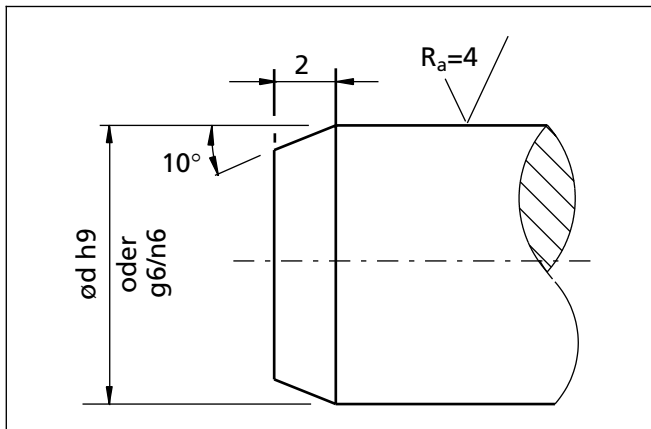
Durchmesser tolerance, Oberflächenrauheit und Kantenfase der Welle
